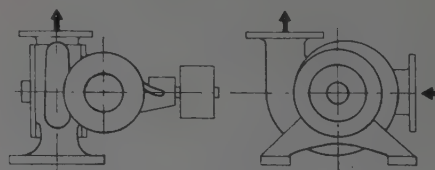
Pompe fixée sur bâti, moteur en porte à faux.
